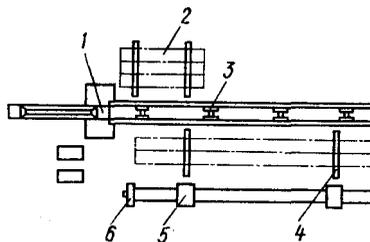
Линия МТЛ для наружной сварки поворотных стыков
